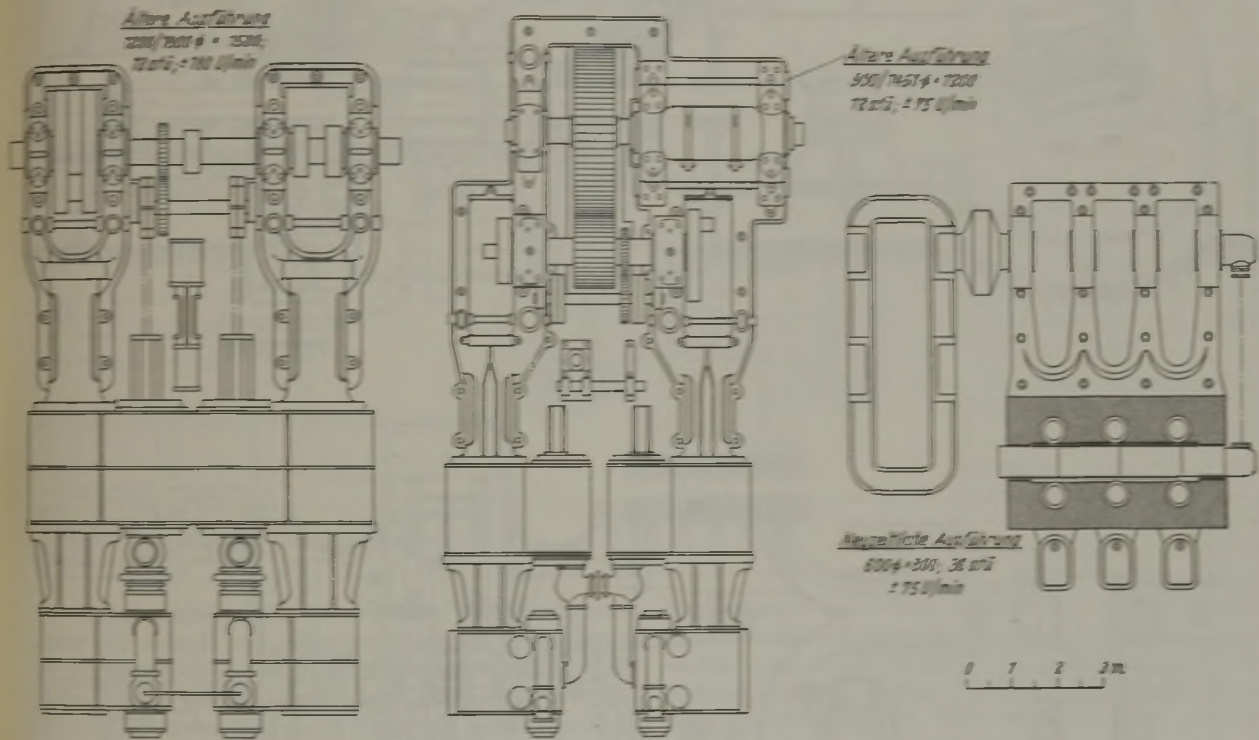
und 3. Platzbedarf von Walzenzug-Umkehrdampfmaschinen mit 180 mt Drehmoment älterer Ausführung im Vergleich mit neuerer Ausführung.
